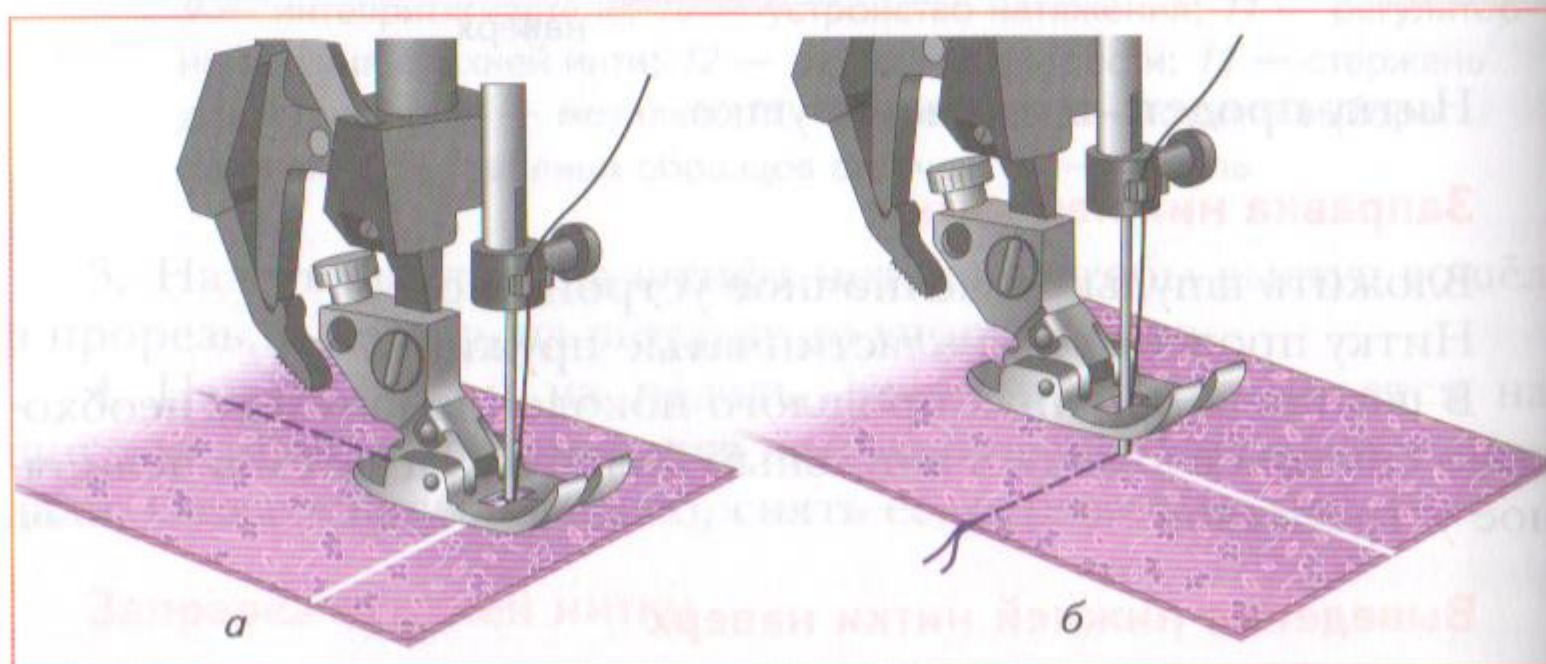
Выполнение поворота строчки под углом: а — лапка и игла опущены; б — поворот ткани при поднятой лапке
